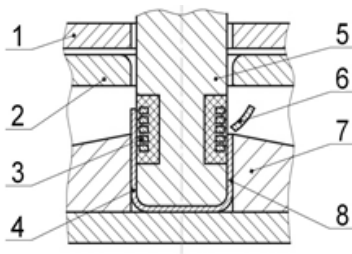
Схема процесса вытяжки и обрезки припуска:
